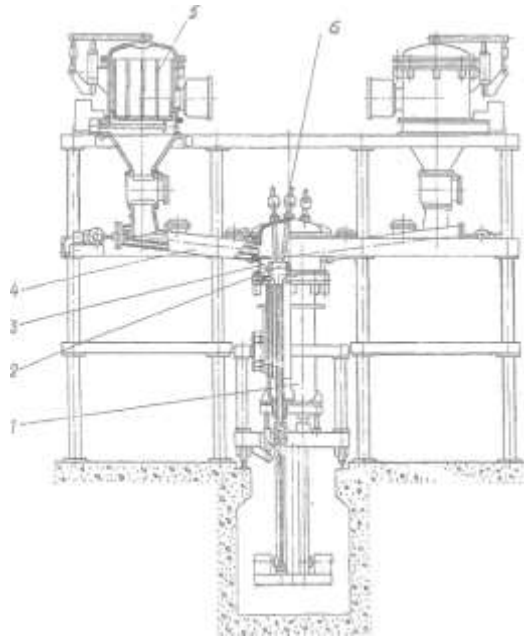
Схема плазмено–дугової печі [93]: 1 – камера зливка з механізмом витягування; 2 кристалізатор; 3 – камера плавильна; 4 віброживильники; 5 – бункер шихтовий; 6 плазмотрон
